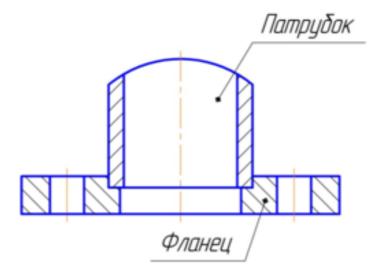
Схема сборки патрубка (поз. 4) с фланцем
